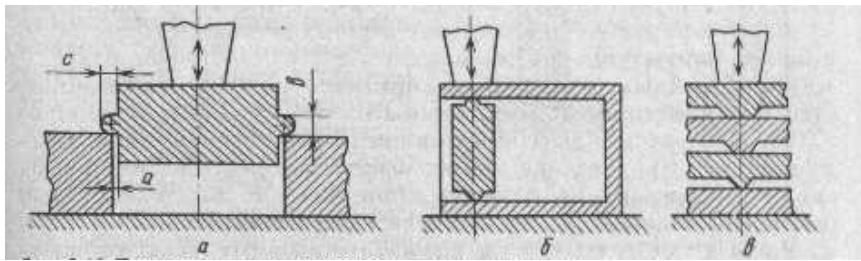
Технологическая подготовка кромок в случаях: а – ультразвукового прессования; б – сварки в двух плоскостях; в – многоэлементной сварки; а = 0,01÷0,25 мм; б = 0,25÷1,25 мм; с = 0,25÷1,25 мм
